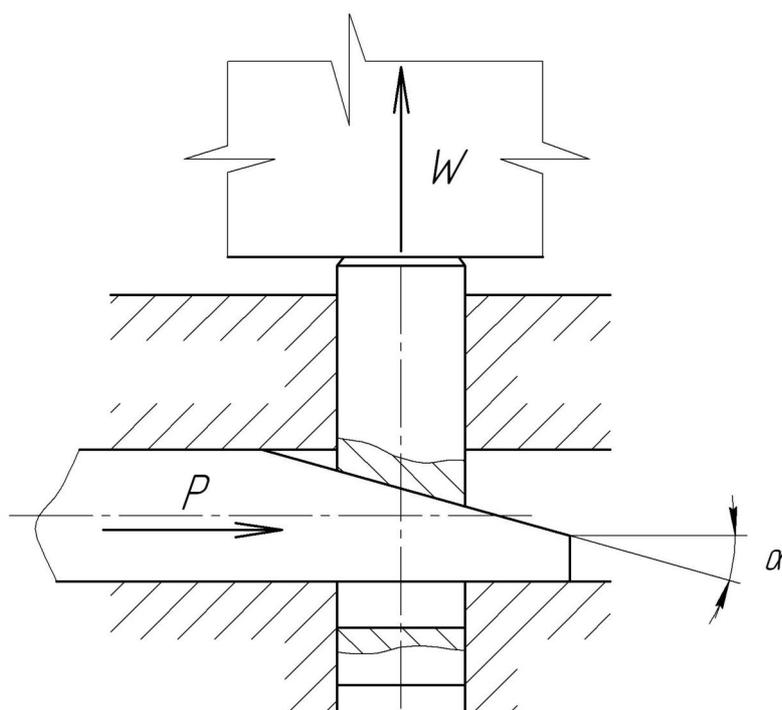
Двухпорный клиноплунжерный зажимной механизм
